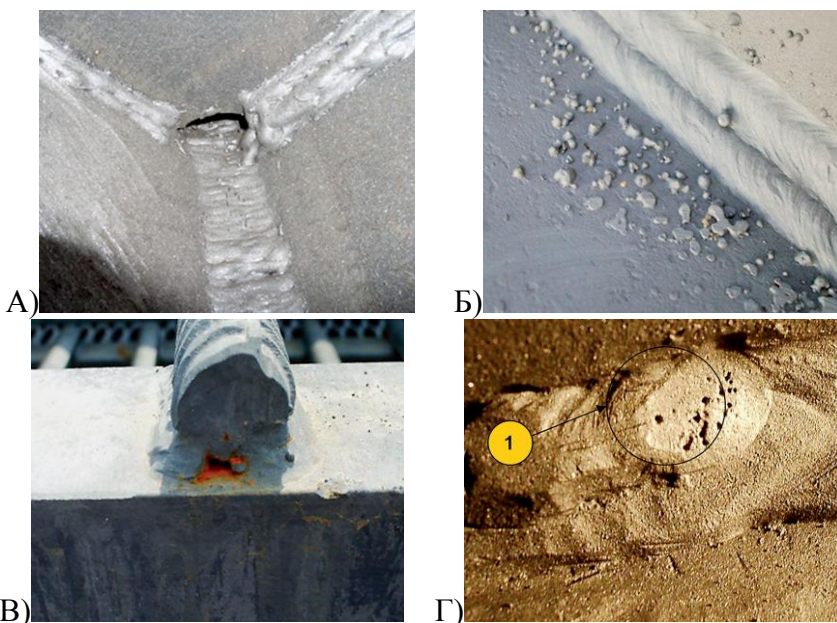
А – Неровный профиль сварного шва, 4Б – Сварочные брызги,
